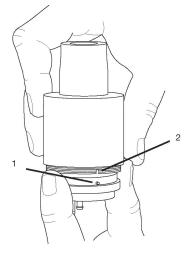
Alignement du capuchon et du corps de la valve expiratoire pendant le remontage
